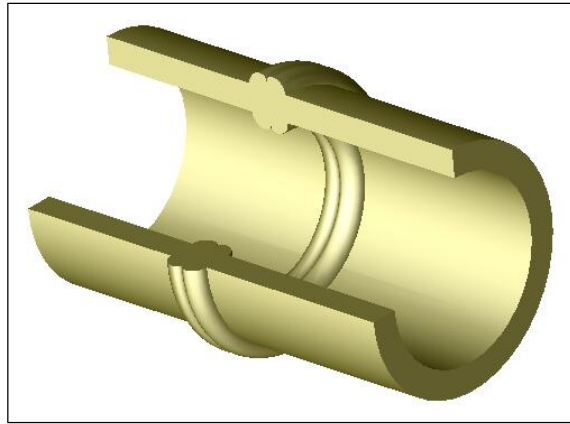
Dibujo de soldadura por termofusión en un tubo.
